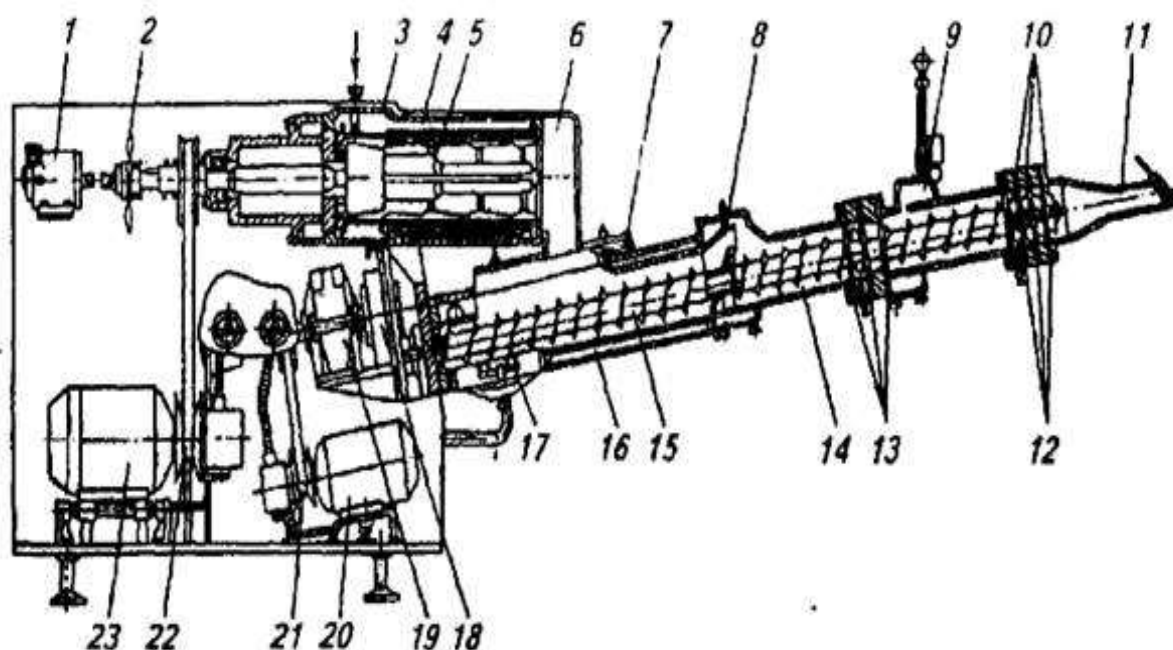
Общий вид маслоизготовителя марки А1-ОЛО/1:
